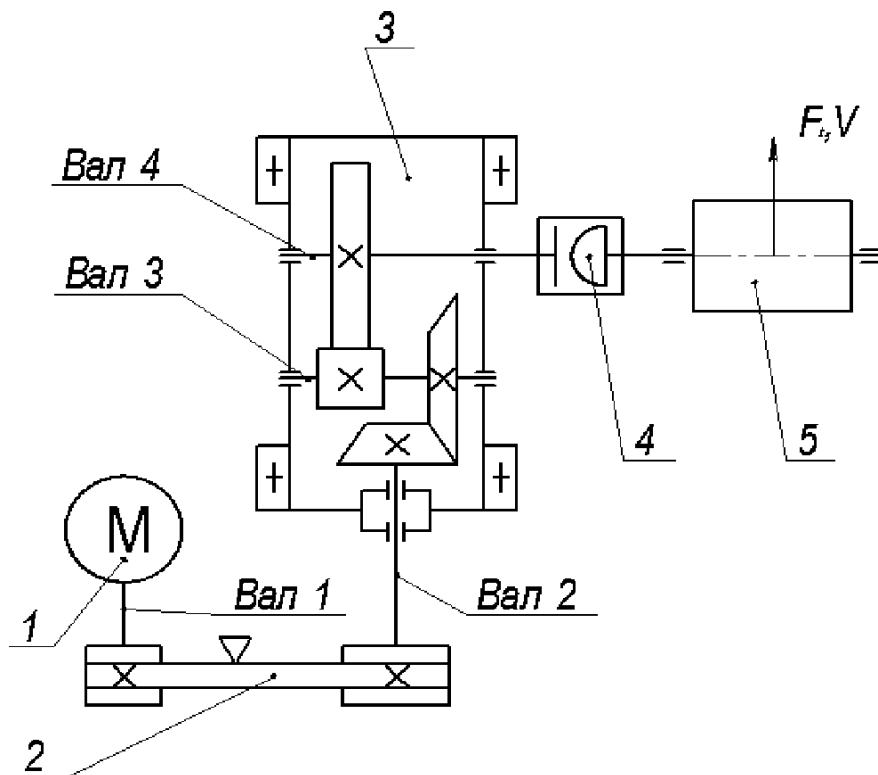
Привід до стрічкового конвеєра: 1 – електродвигун; 2 – ремінна передача; 3 - конічно-циліндричний редуктор; 4 – муфта фрикційна; 5 - приводний барабан
